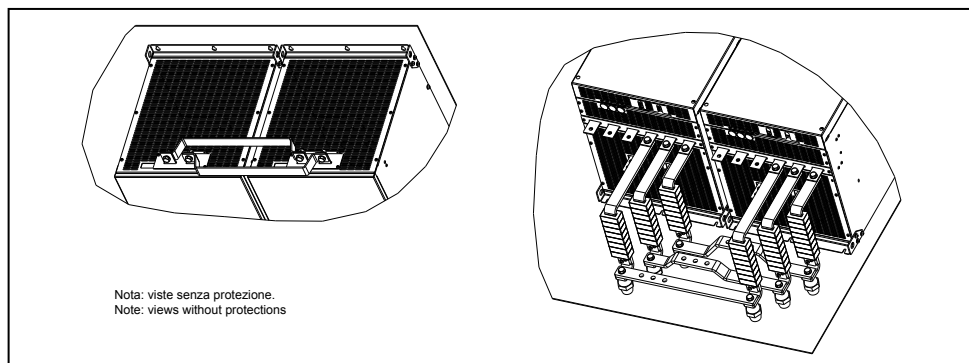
Набор шин для типоразмеров 400 ... 710 кВт
